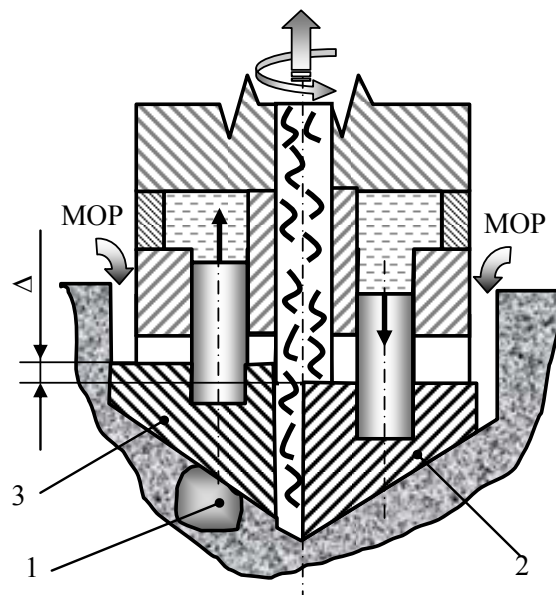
Кінематична схема роботи свердла з міжлезовим гідравлічним зв'язком
